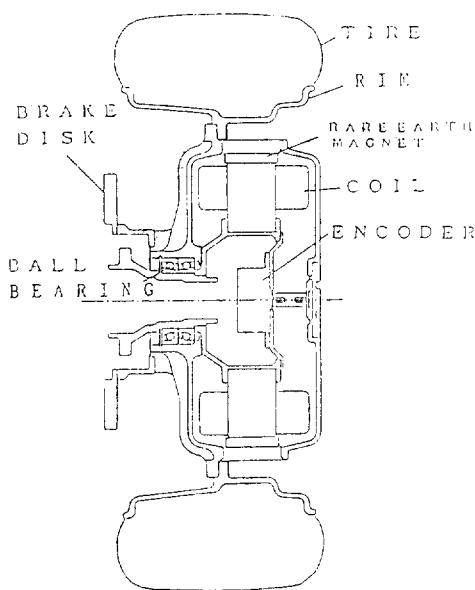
바퀴에 직접 장착된 outer-Rotor type BLDC motor(IZA)
